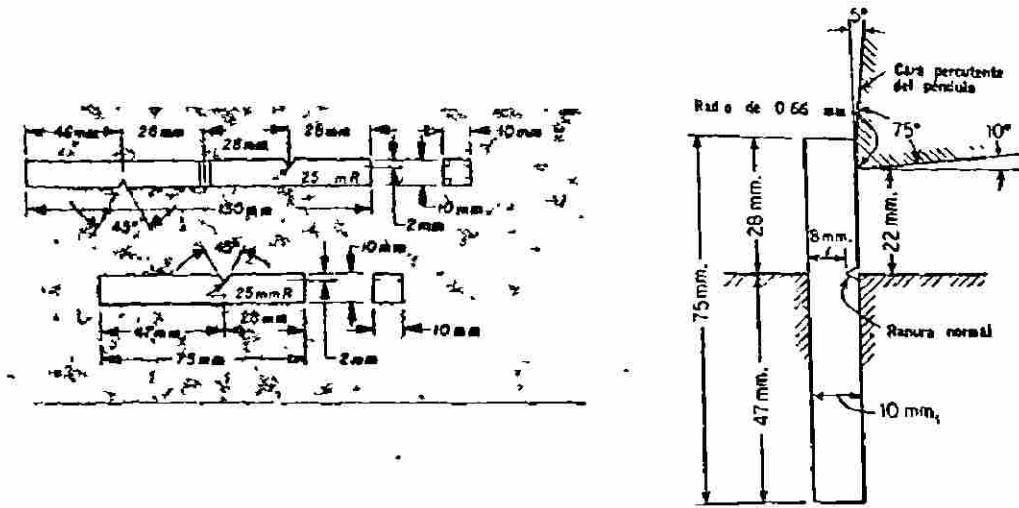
Probeta de viga en voladizo y su montaje para el ensayo de Izod.
